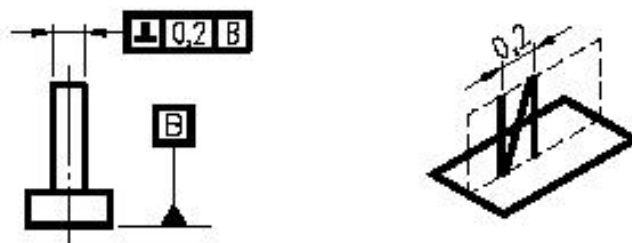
Tolerância de perpendicularidade – especificação em desenho e interpretação.
